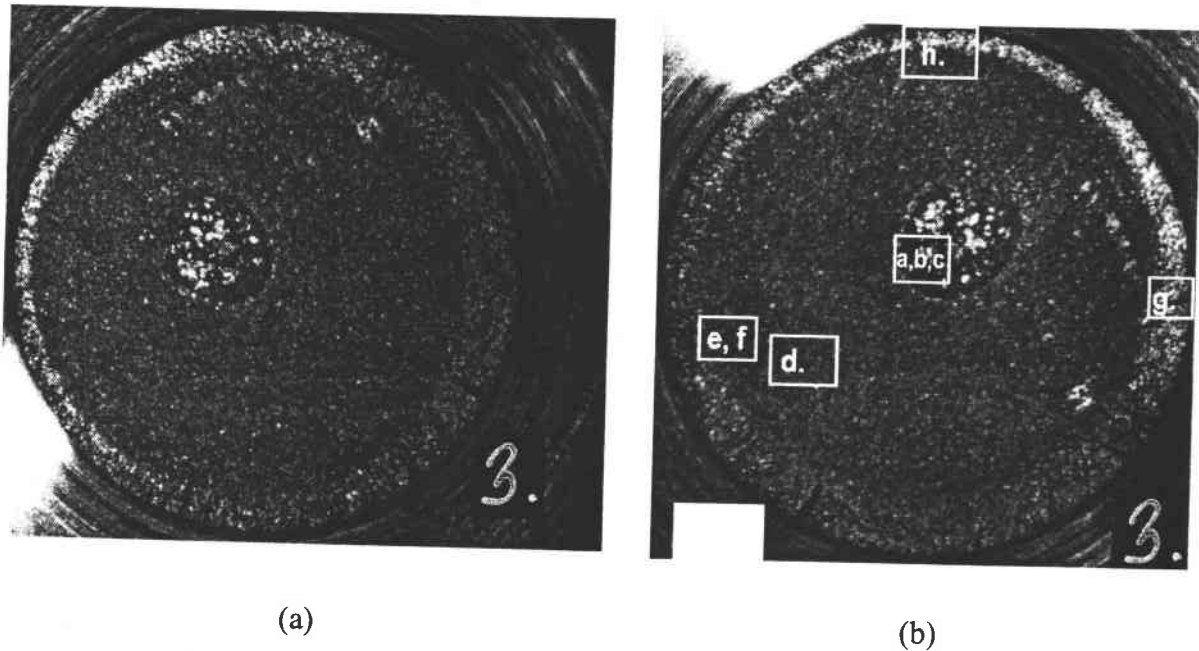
Aspect macroscopique d'éprouvettes entaillées ($\rho = 0,2 \text{ mm}$) soumises au chargement de flexion rotative: a) vue générale b) division de la surface.
